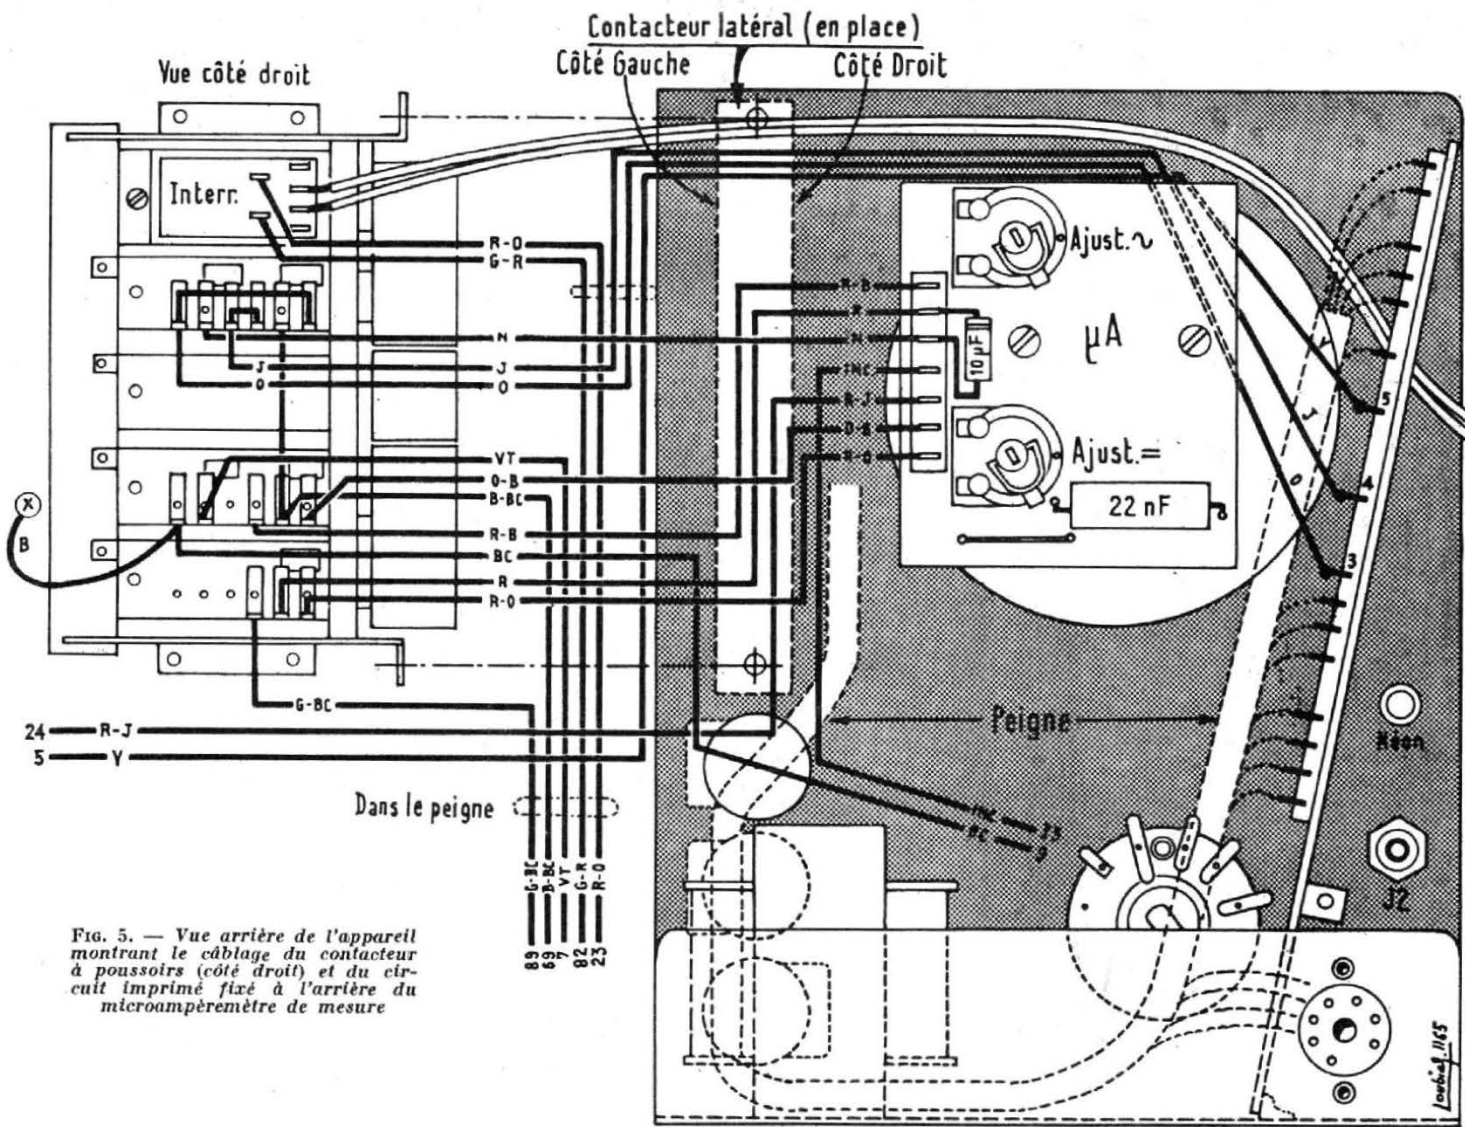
Vue arrière de l'appareil montrant le câblage du contacteur à poussoirs (côté droit) et du circuit imprimé fixé à l'arrière du microampère de mesure
